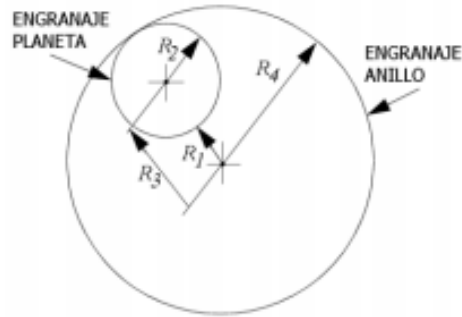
Tren de engranajes planetarios: Radios de los engranajes
